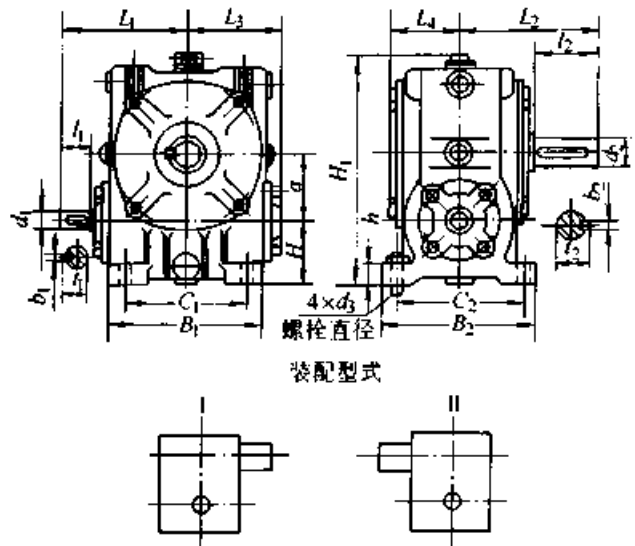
KWU 型减速器的外形尺寸和装配型式
